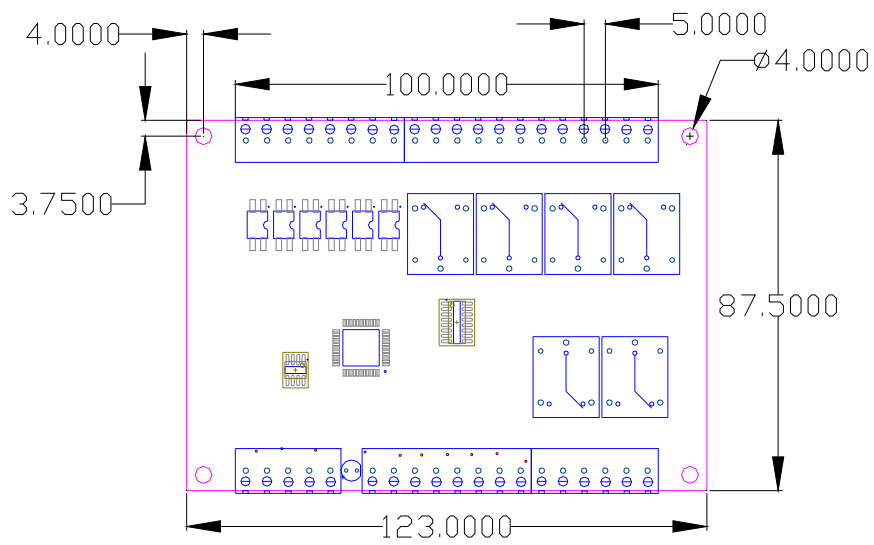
电路板尺寸图 (PCB 板厚 1.6mm, 上层元件最高 15.5mm)
